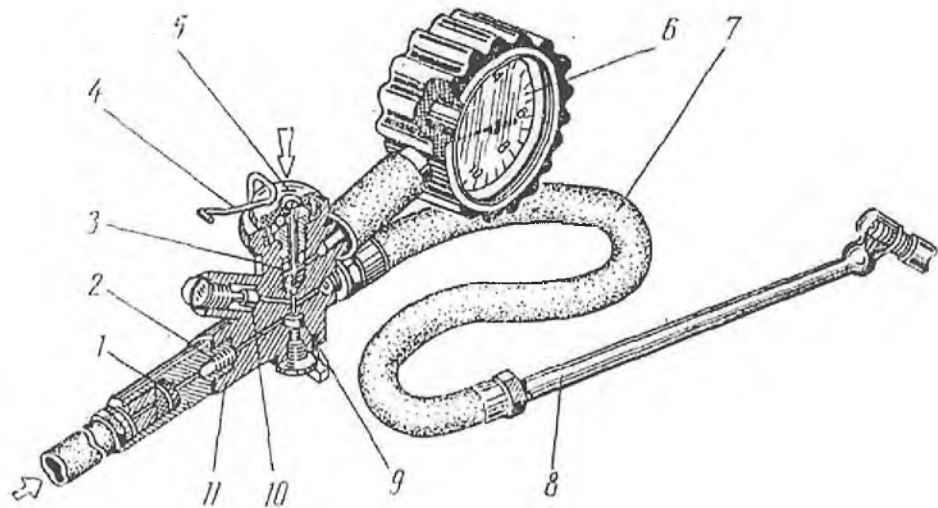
Наконечник с манометром для воздуховоздухораздаточного шланга:
